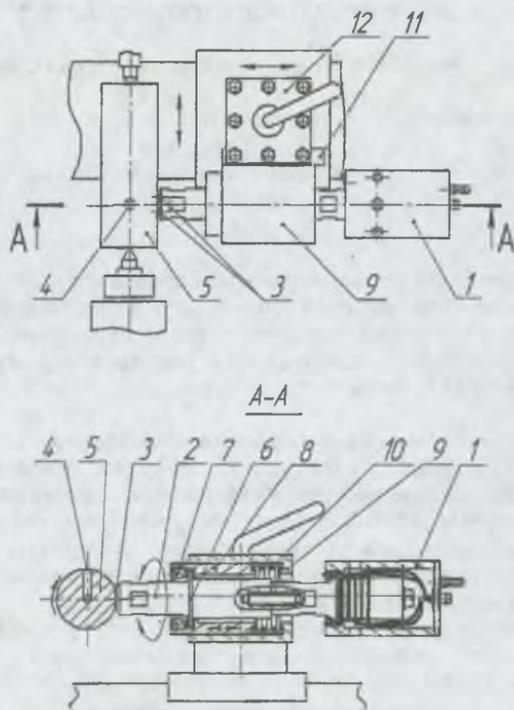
Конструкция устройства для упрочняюще-чистовой обработки и схема его монтажа в резцедержателе суппорта токарного станка
